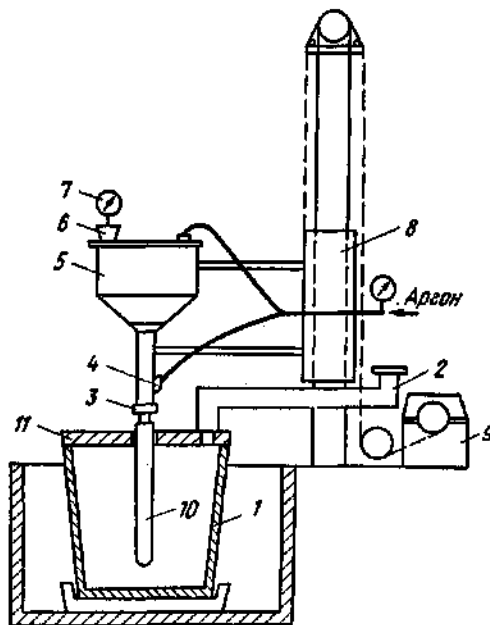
Схема полупромышленной установки по обработке стали в ковше порошкообразными реагентами:
